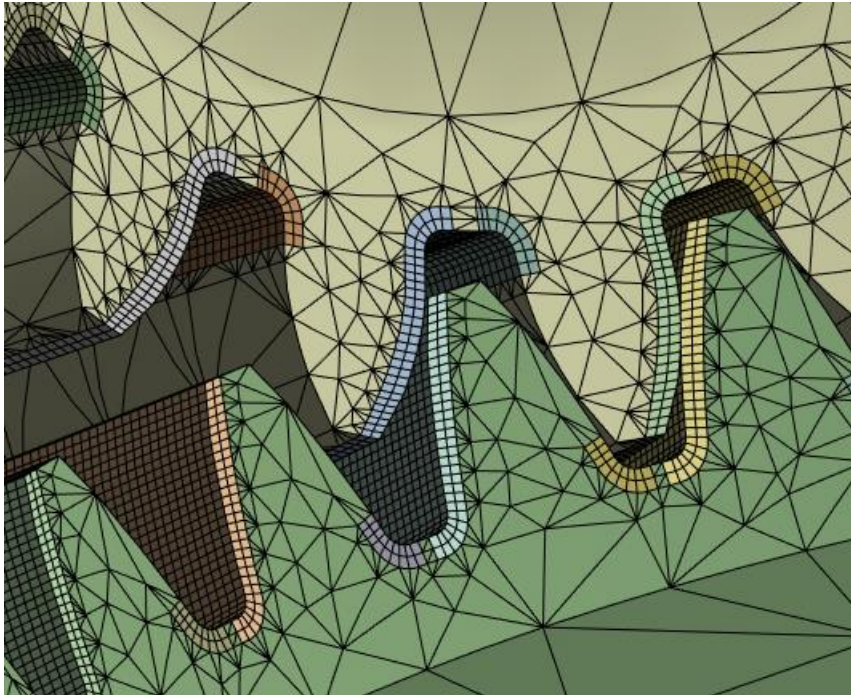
Zobrazení kontaktů soukolí bez modifikace
